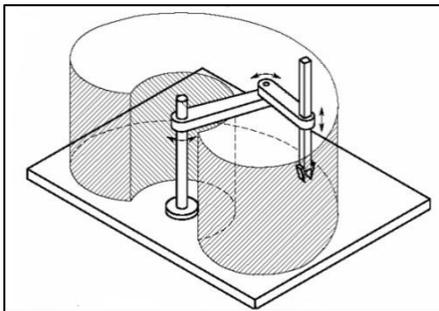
Geometria SCARA (Melchiorri, 2002)
